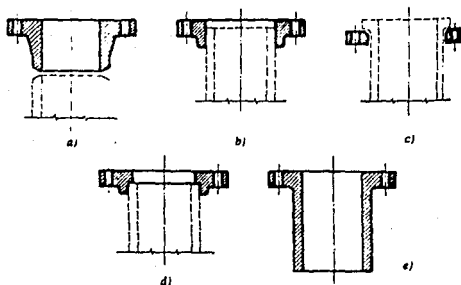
Tipos de bridas. a) Para soldar a tope. b) Para soldar sobrepuesta. c) Libre. d) Para soldar a enchufe. e) Brida para soldar a tope largo.
